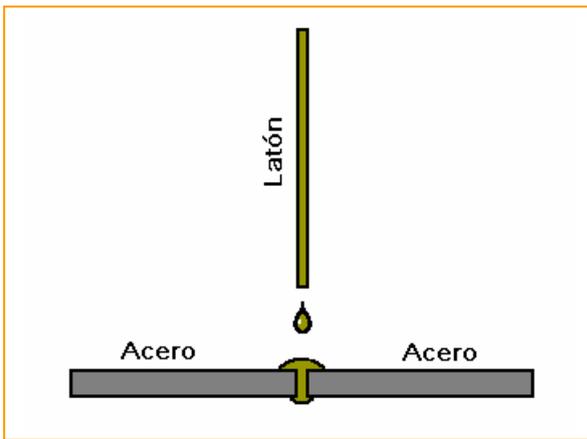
Ejemplo de soldadura heterogénea.
